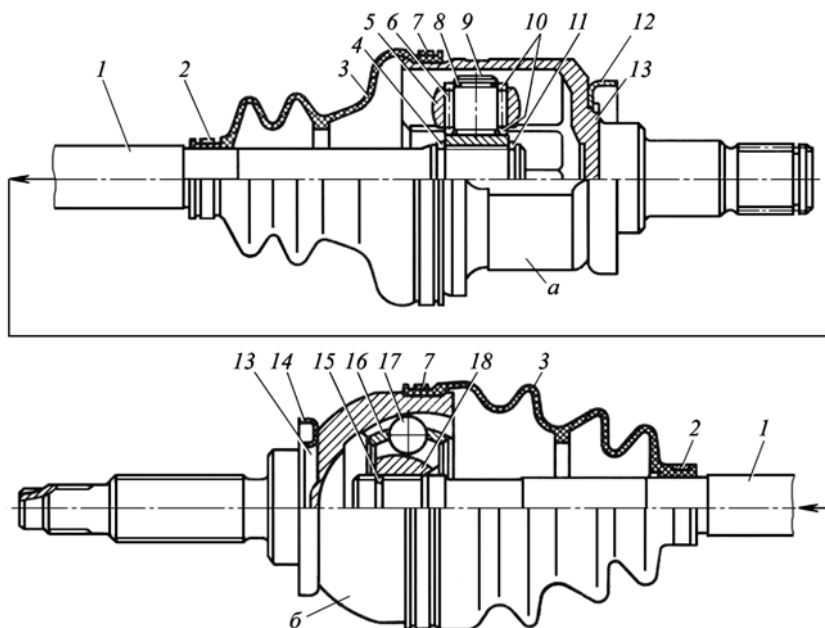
Внутрішній (а) і зовнішній (б) шарніри шарнірного вала автомобіля ЗАЗ-1102:
